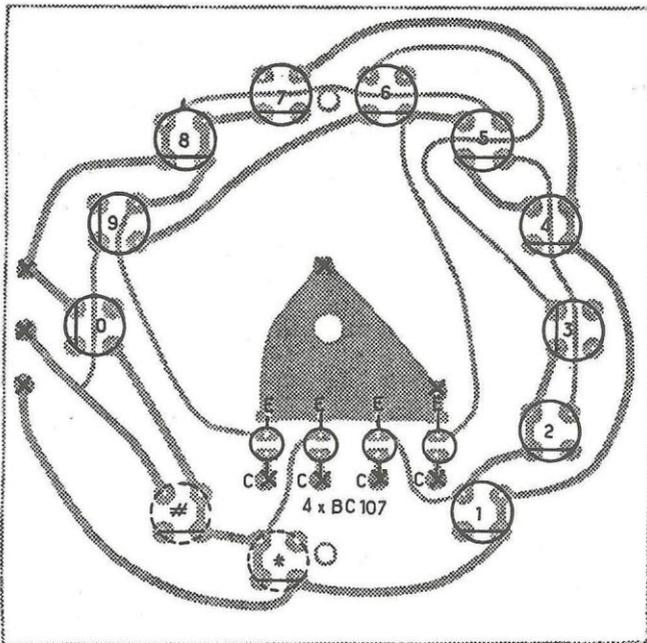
Montaje de los componentes del circuito impreso principal.
